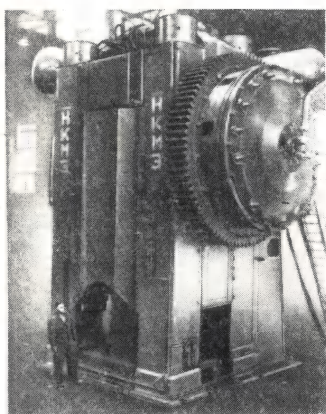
Кривошипный горячештамповочный пресс с усилием 6 300 т.
